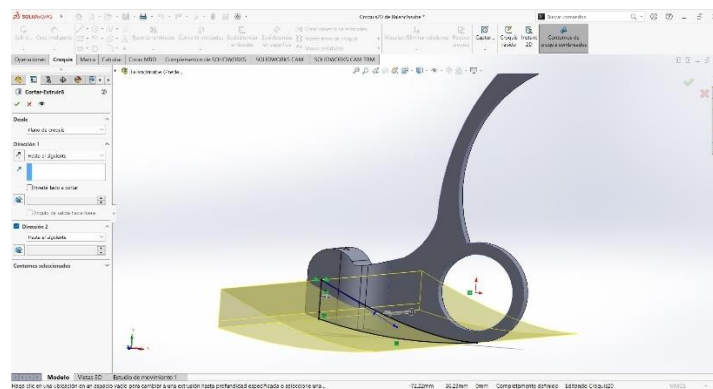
Balancín 1 (Extrusionado de corte de Croquis 7). Fuente: SolidWorks
